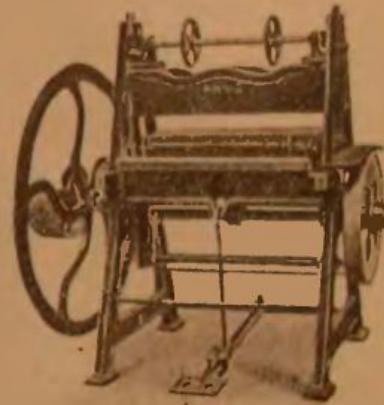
Эксцентриковый штамповочный пресс для пожного или механического привода.
